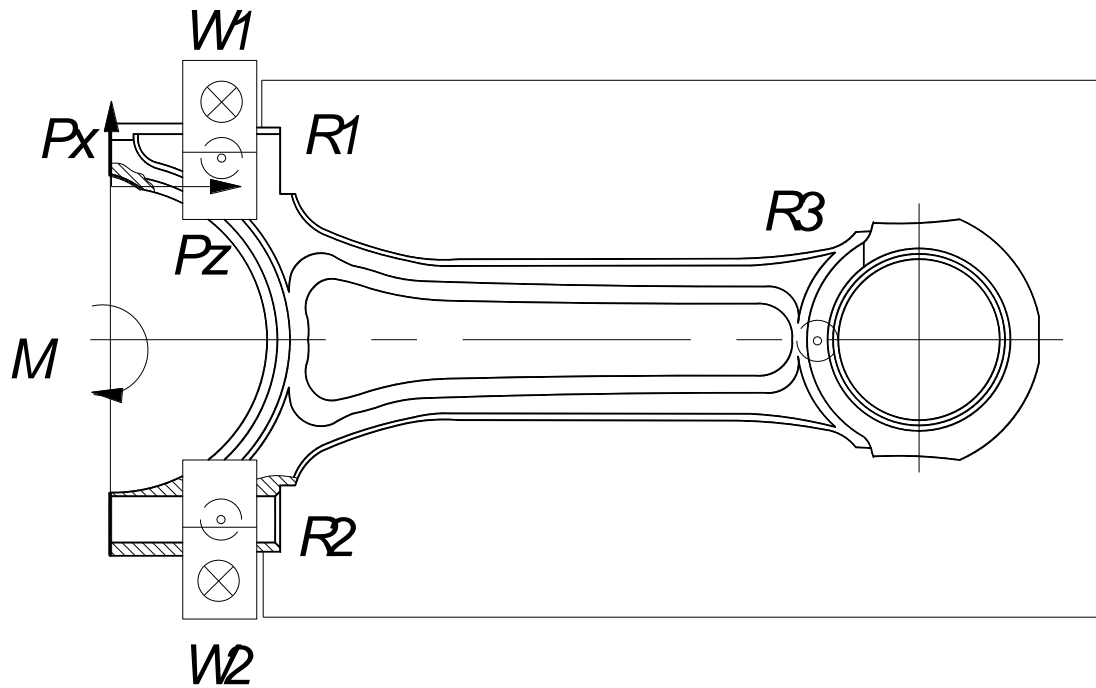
Схема сил, що діють на шатун при фрезеруванні паза
